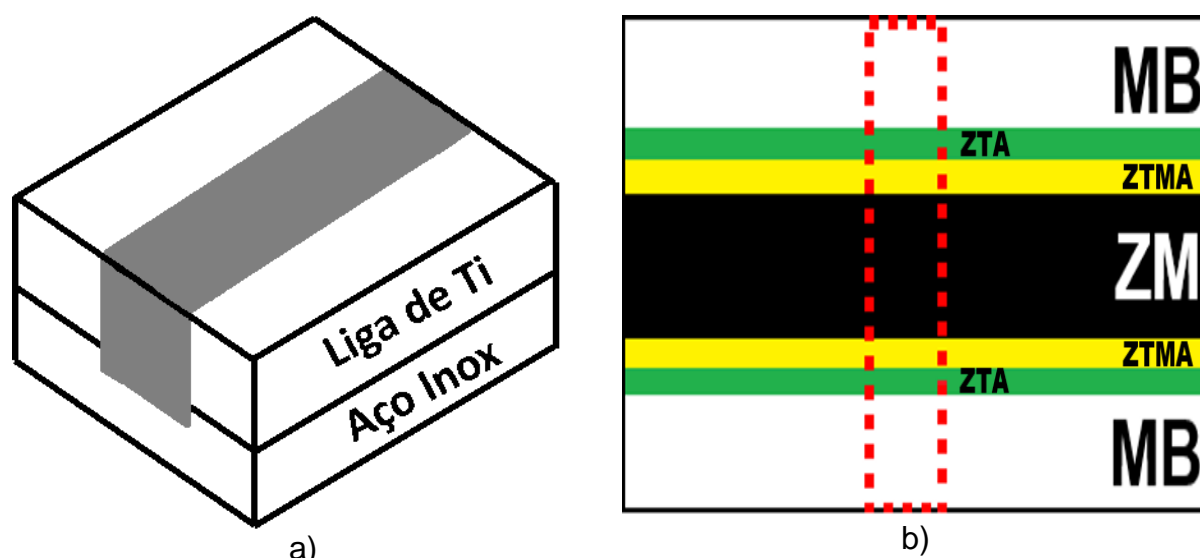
a) Configuração das placas da liga de Ti e do aço inoxidável durante o processo de soldagem por fricção linear e b) regiões afetadas (ZM, ZTMA e ZTA) ou não (MB) pela solda na chapa da liga de Ti. A região escura indica o local onde a solda foi efetuada (Fonte: próprio autor).
